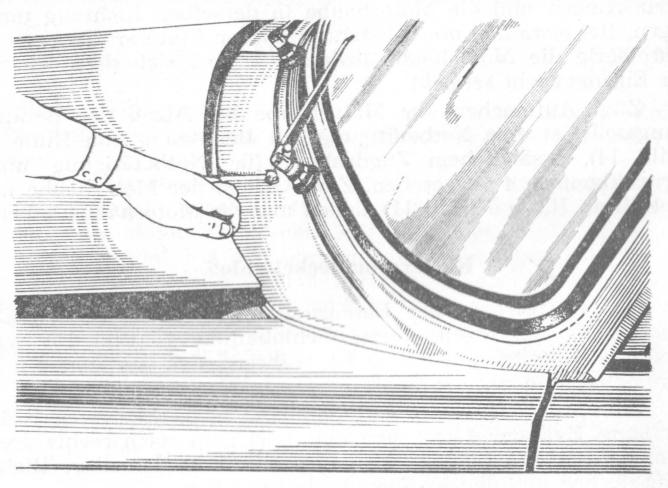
Fassen der entriegelten Motorhaube mit der Hand
